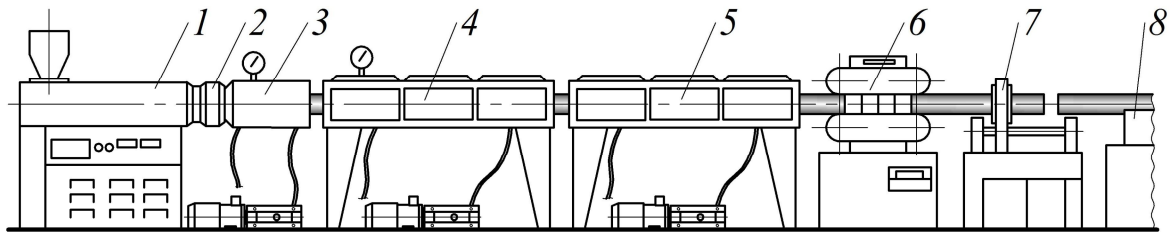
Принципова схема виготовлення труб [65]: 1 – екструдер, 2 – трубна головка, 3 – калібрувальний пристрій, 4 – вакуум-ванна, 5 – ванна зрошення, 6 – тягнучий пристрій, 7 – відрізний пристрій, 8 – приймальний пристрій
